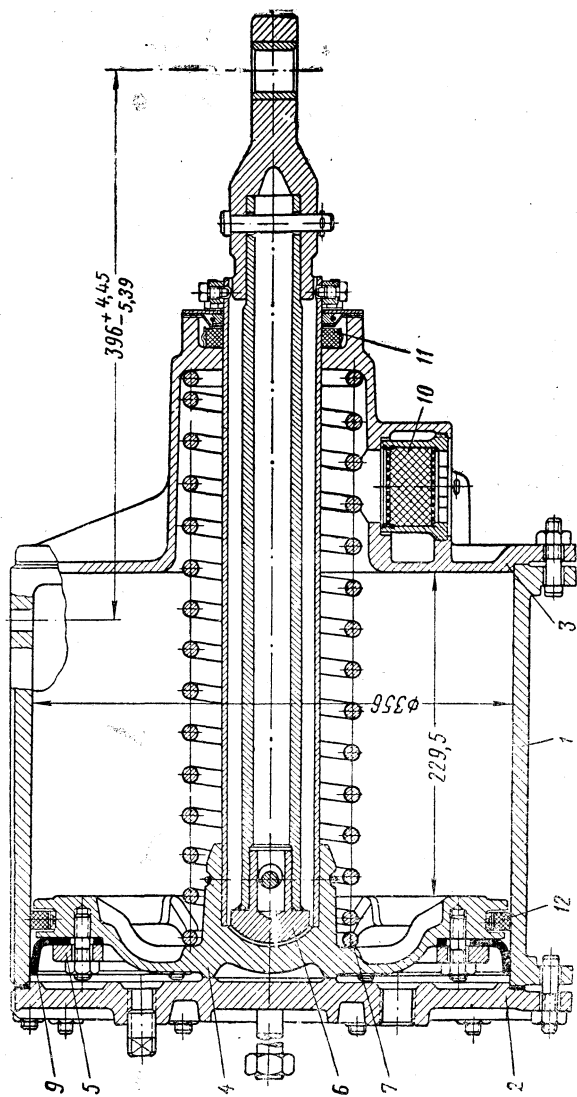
Тормозной цилиндр 14" усл. № 188: 1 — корпус; 2 — крышка задняя; 3 — крышка передняя; 4 — диск поршня; 5 — шайба поршневая; 6 — шток поршня; 7 — пружина отжимающая; 9 — воротник; 10 — фильтр (рис. 136); 11 — сальник (рис. 137); 12 — смазывающее кольцо
